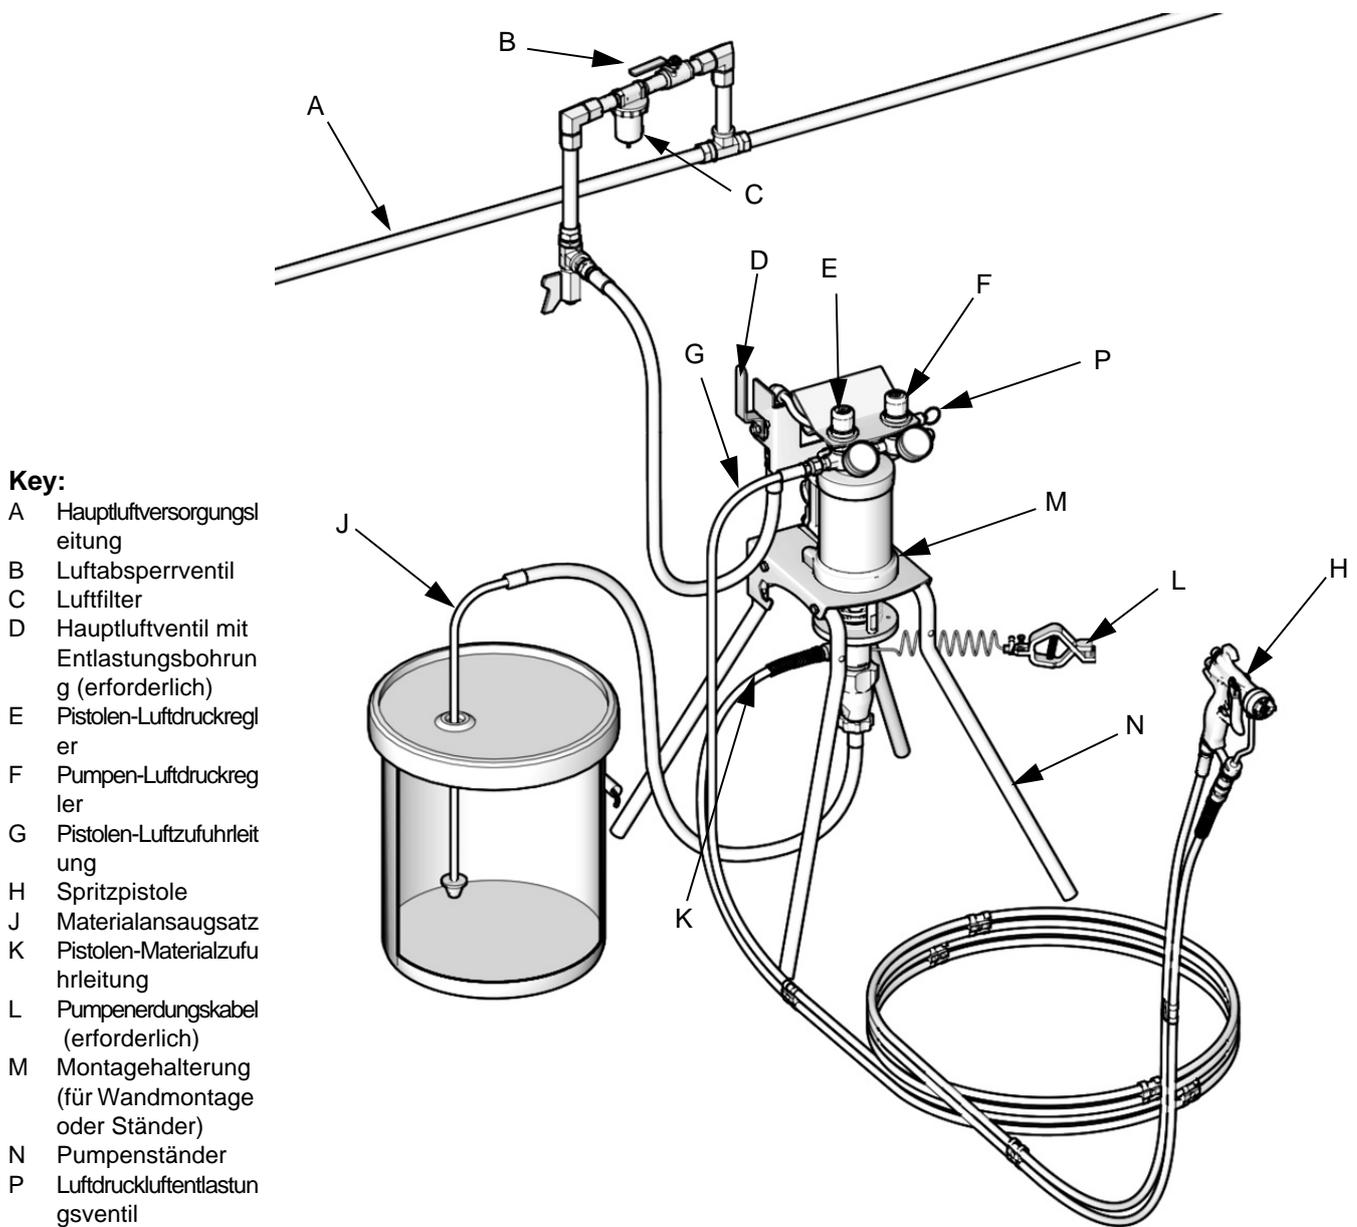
Typische Installation (luftunterstütztes Komplettgerät für Ständermontage abgebildet)
